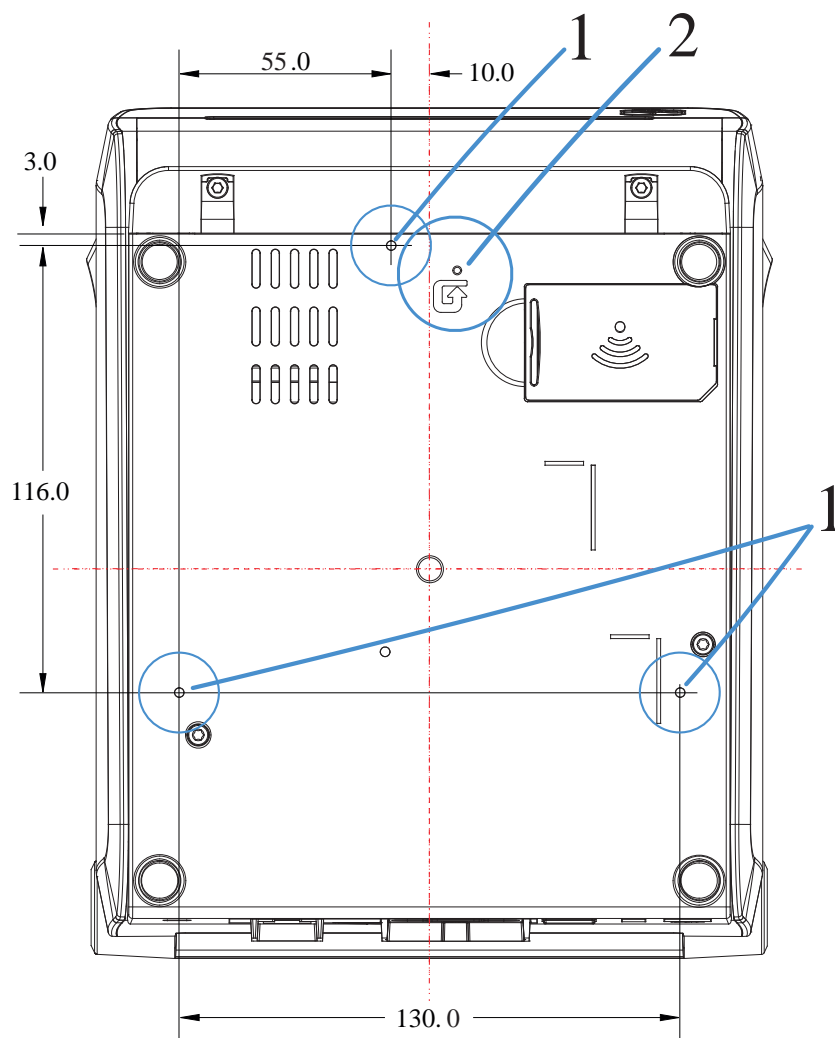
Imprimante thermique directe ZD621 (modèles Healthcare uniquement) avec armoire pour supports verrouillable : dimensions
